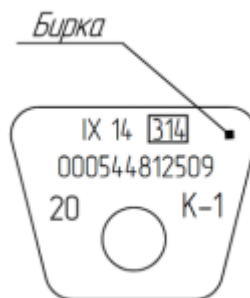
Бирка буксового узла с подшипником кассетного типа в габаритных размерах 130x250x160 торговой марки Бренко
